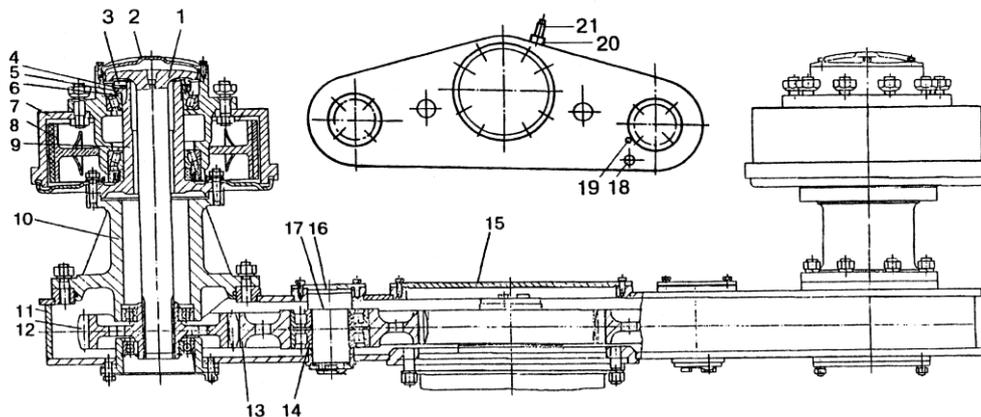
Балансир автогрейдера А120: 1 – полуось; 2 – крышка ступицы колеса; 3 – контргайка подшипников колеса; 4 – замочная шайба; 5 – гайка подшипников колеса; 6 – конический подшипник; 7 – ступица с тормозным барабаном; 8 – тормоз; 9 – цапфа; 10 – корпус; 11 – корпус редуктора; 12, 13 – шестерни; 14 – подшипник; 15, 16 – крышки; 17 – ось; 18 – магнитная пробка сливного отверстия; 19 – коническая пробка контрольного отверстия; 20 – пробка заливного отверстия; 21 – сапун
